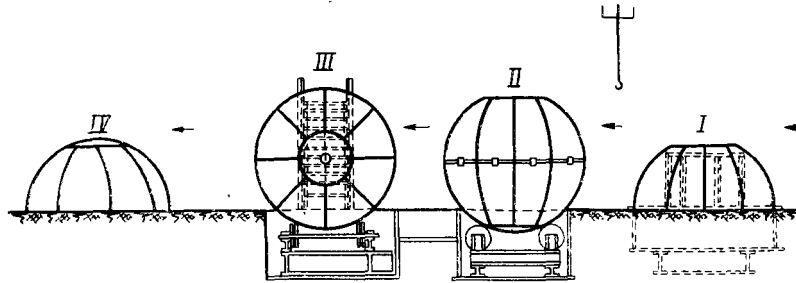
Схема технологического процесса сборки и сварки полусферических днищ
